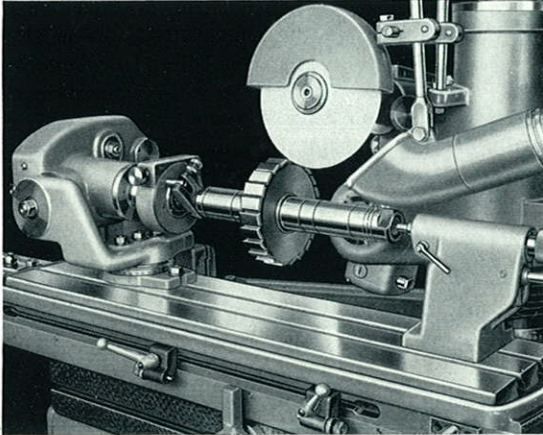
Schleifen der Spanfläche eines hinterdrehten Nutenfräasers mit AT III. Bild zeigt ferner die Radialzustellung
